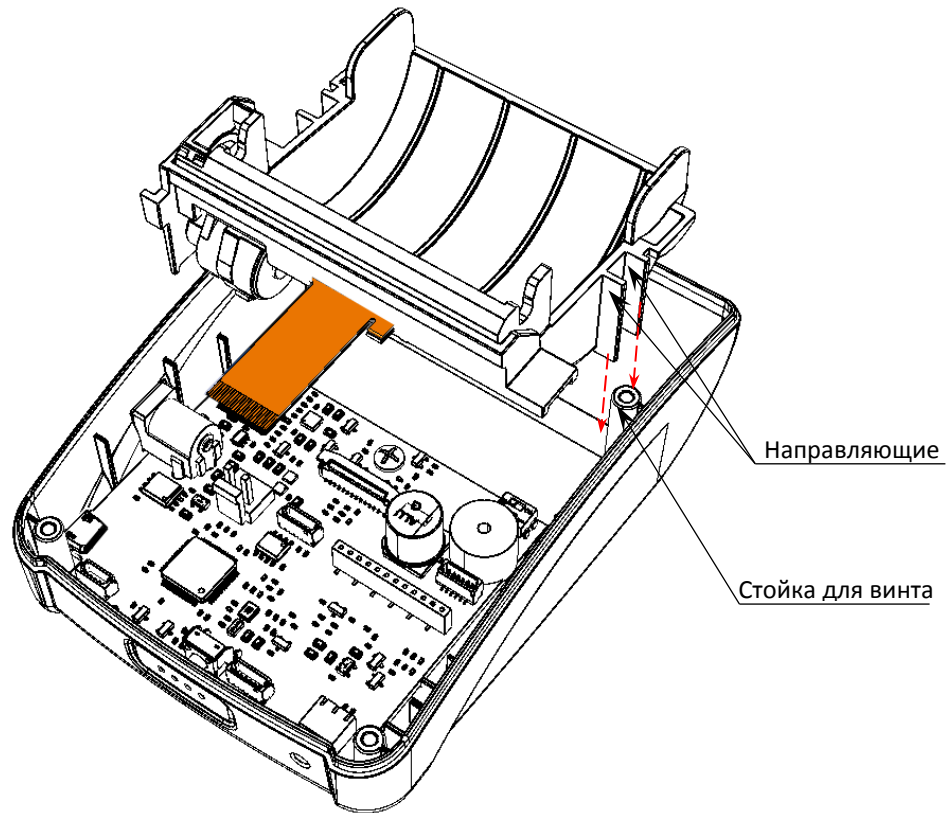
Установка лотка для ЧЛ в нижнюю часть корпуса ККТ
